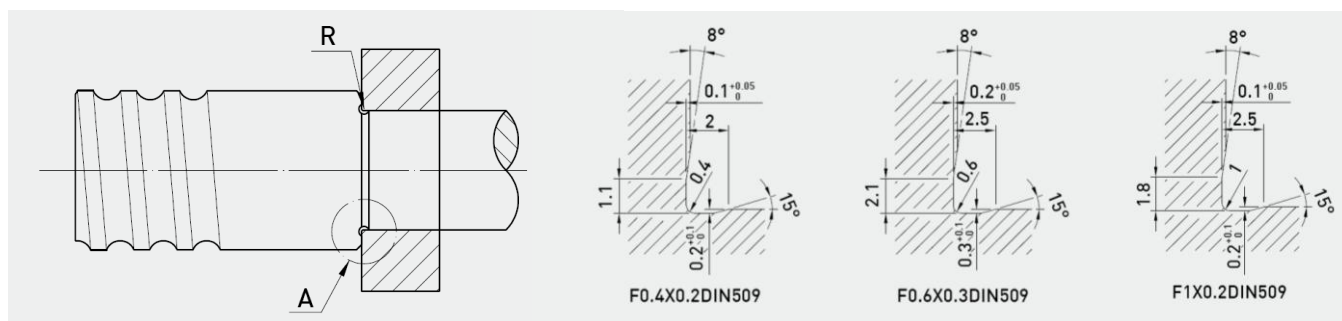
Схема обработки торцов упорной поверхности и кольцевая проточка по DIN 509
